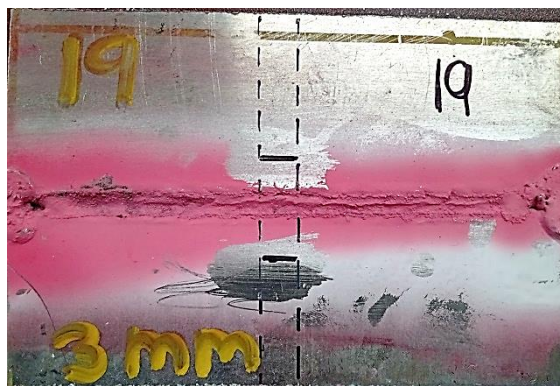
61 Seccionamiento transversal de la soldadura 19 de aleación de aluminio 5052-H32 unido por el proceso GMAW robotizado.
